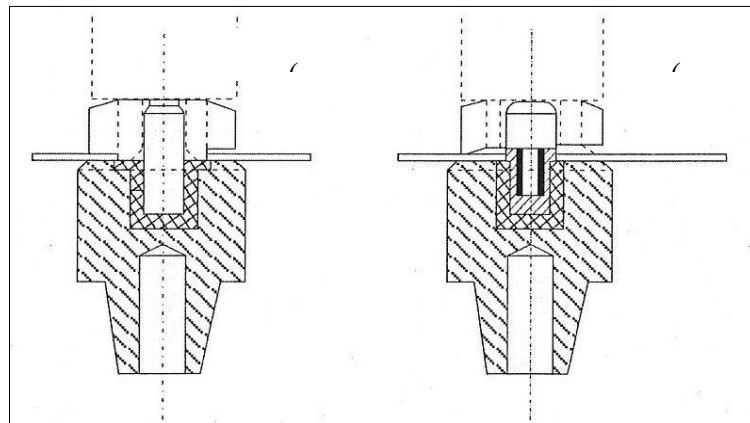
Pines centradores para soldadura de tuerca con cuello centrador (a) y sin ellos (b).
